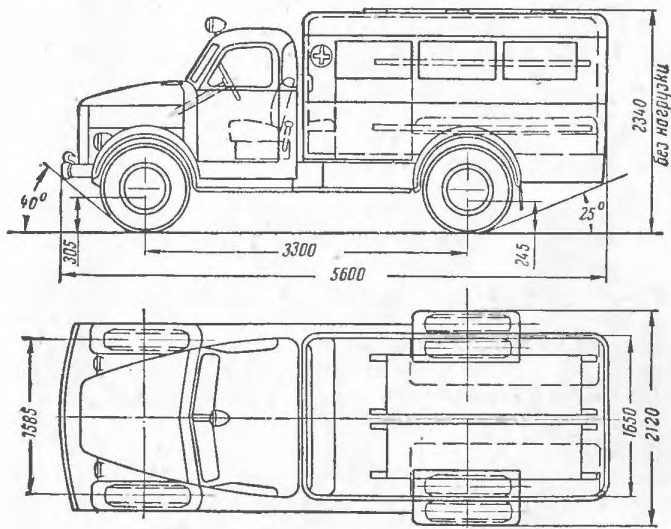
Схема санитарного автомобиля ПАЗ-653.
